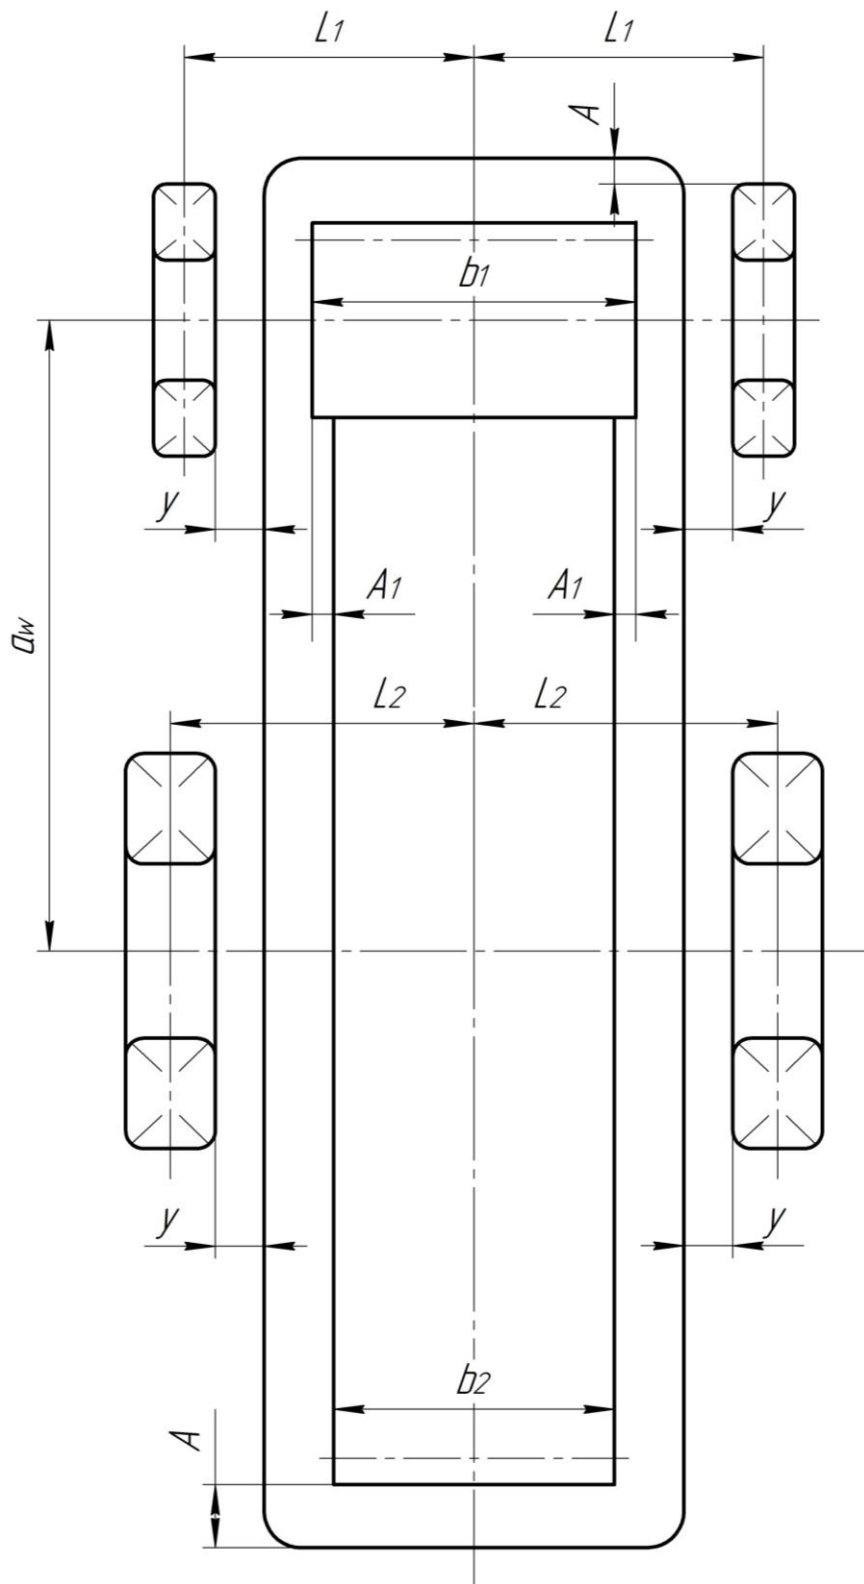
Попередня компоновка одноступеневого циліндричного редуктора
